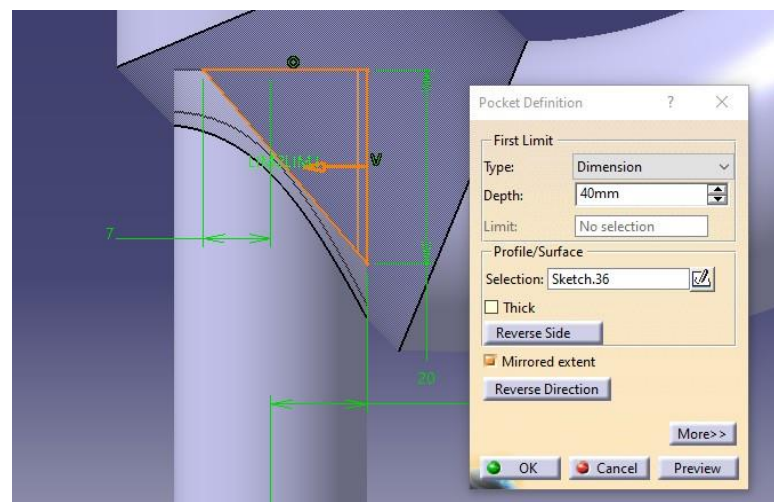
Обробка торця заправної труби методом фрезерування.
